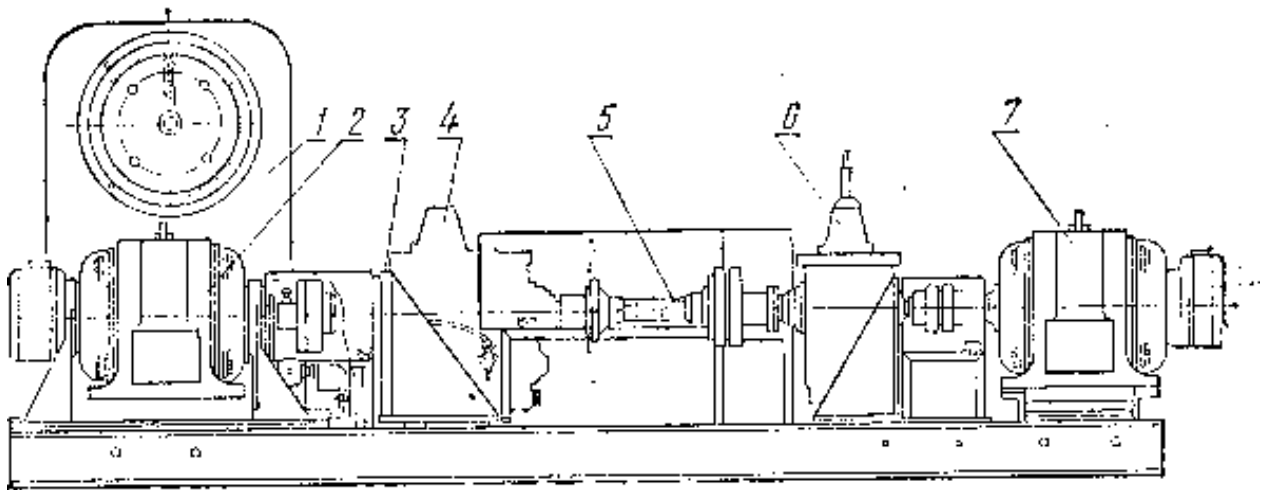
Стенд для обкатки і випробування коробок передач:
